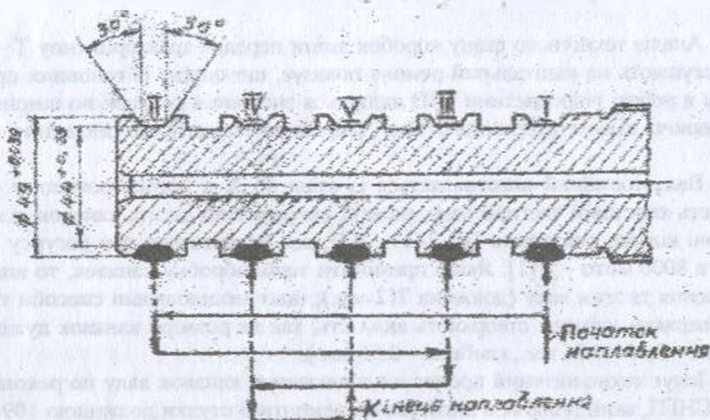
Схема підготовки та наплавлення канавок вторинного валу.
